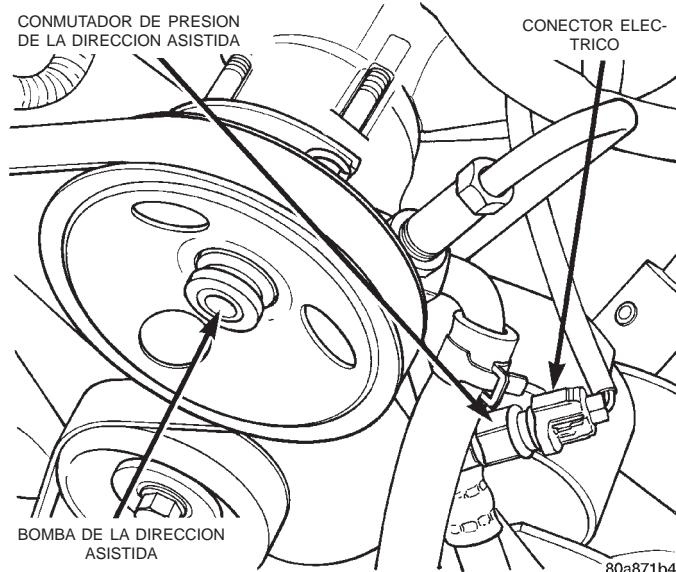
Conmutador de presión de la bomba de la dirección asistida—motor 2.5L
